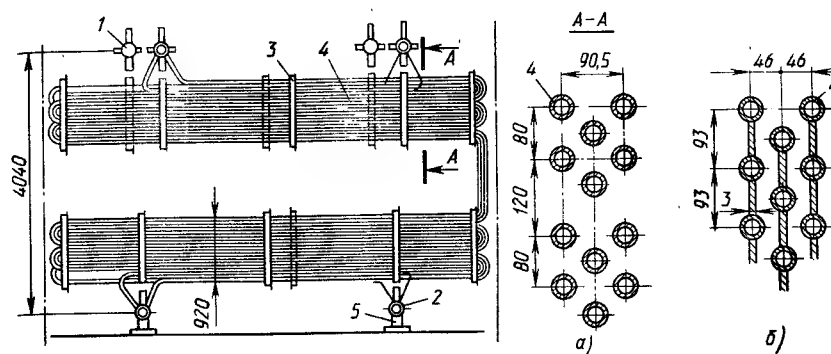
Ступень двухпоточного экономайзера прямооточного котла
